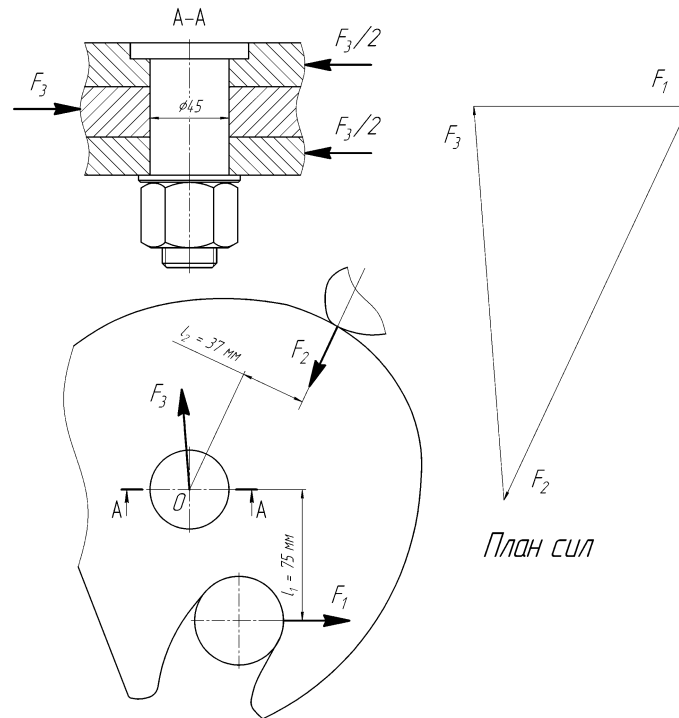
Розрахункова схема захвата сидельно-зчіпного пристрою
